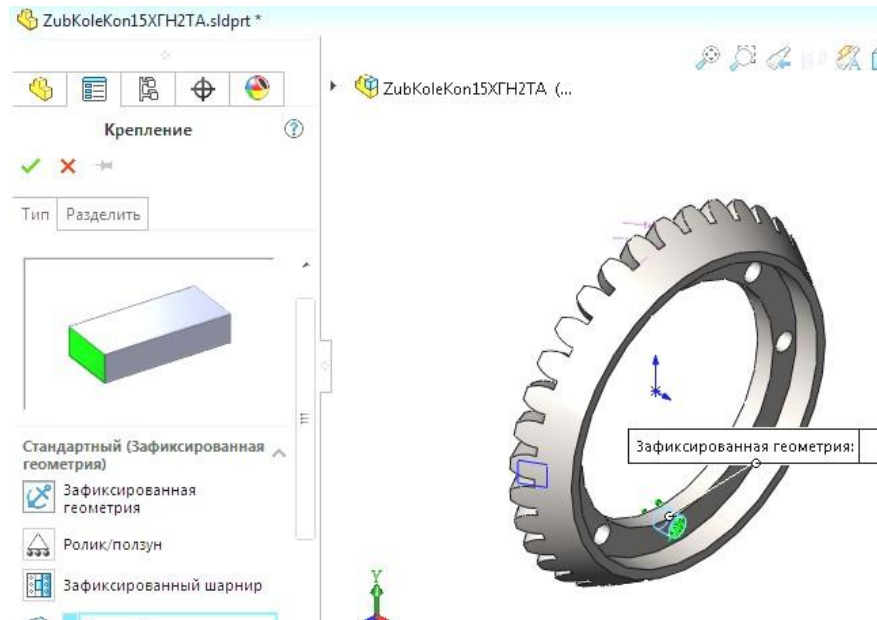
Визначення точок підтримки для зубчастого конічного колеса.
